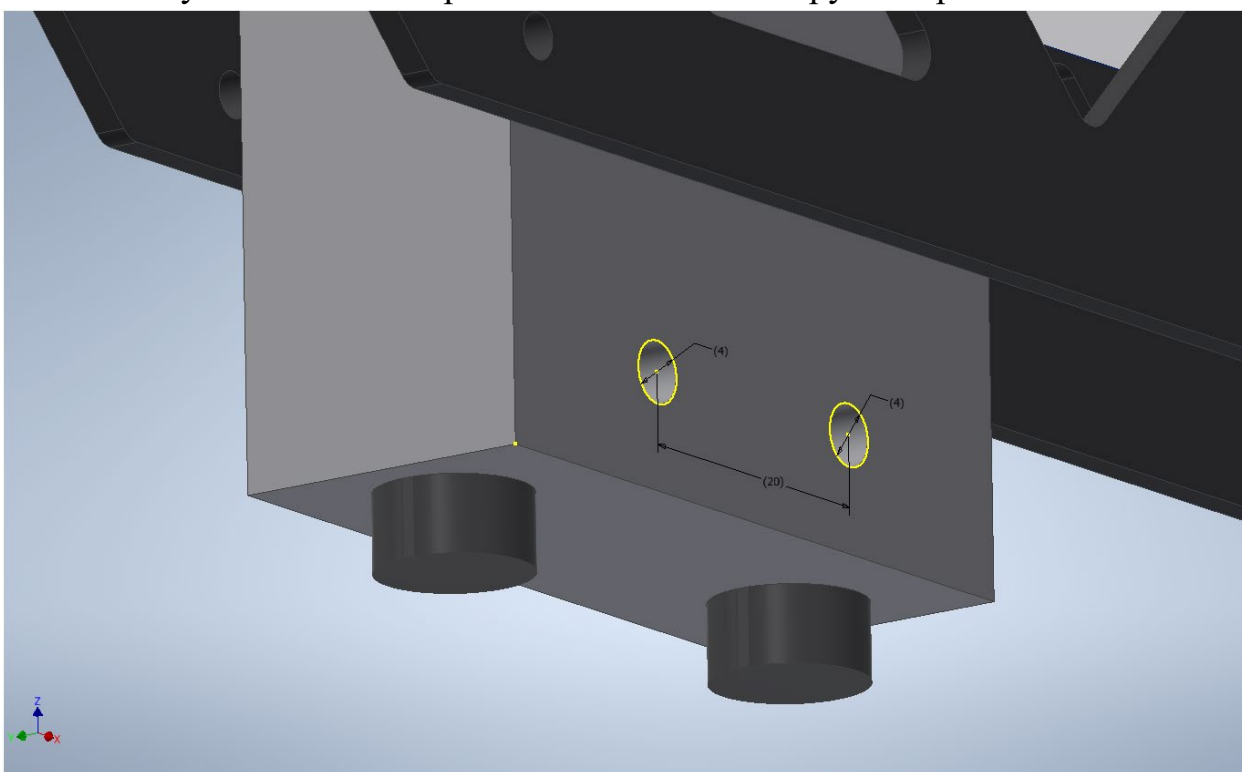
Размеры и расположение отверстий места крепления ПН.
